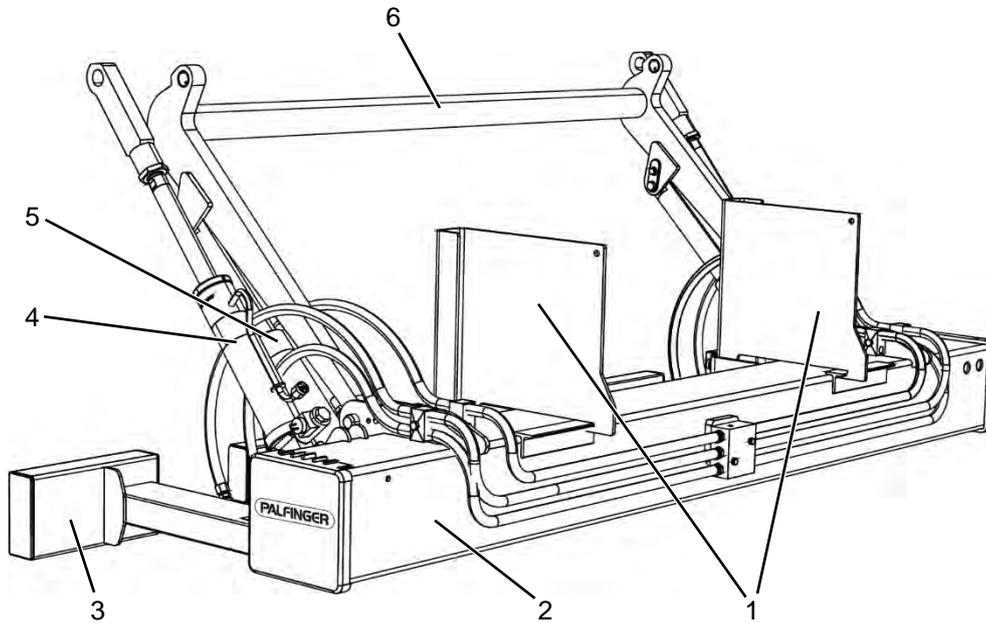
Trampilla elevadora con ménsulas atornillables y grupo enchufable
